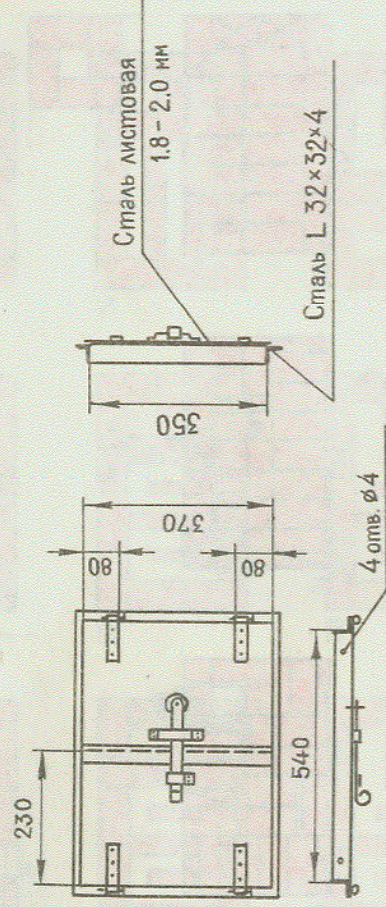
Рамка с дверкой для варочной камеры печи Ш-5.
